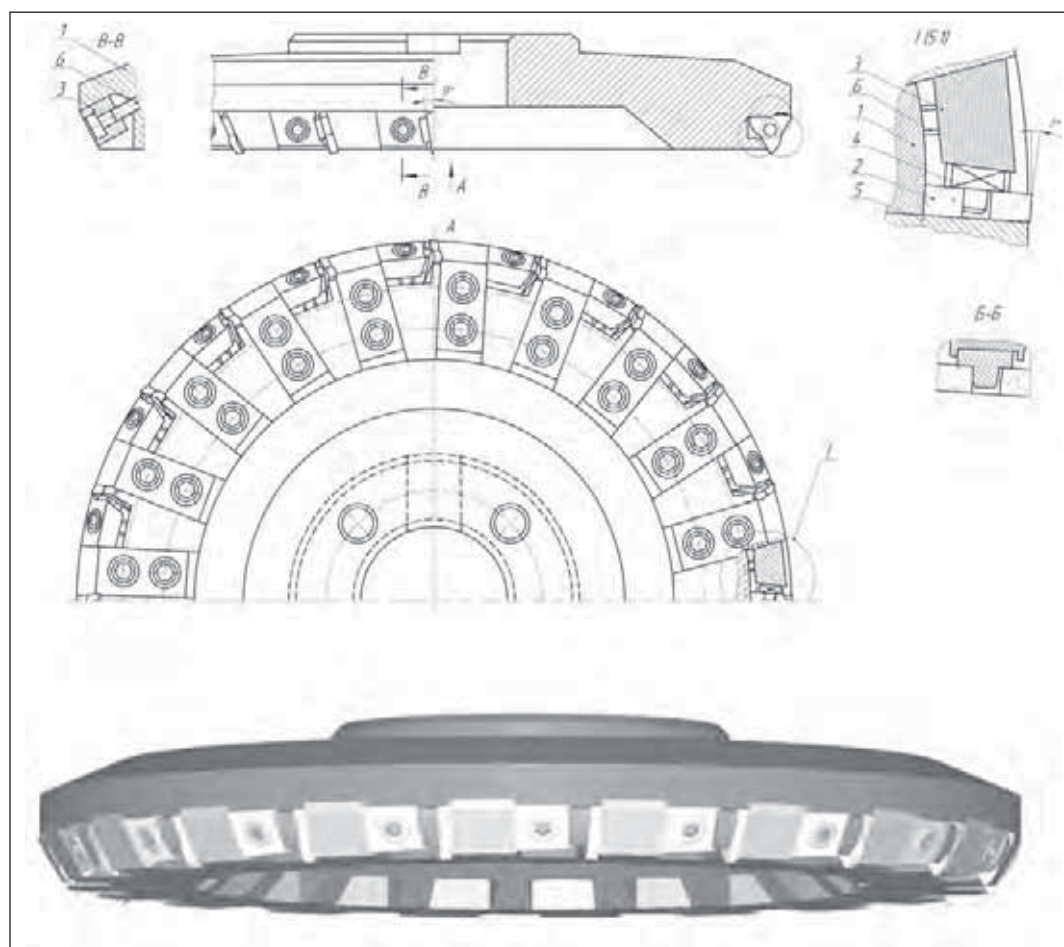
Разработанная конструкция торцевой фрезы с пластинами высокой прочности
